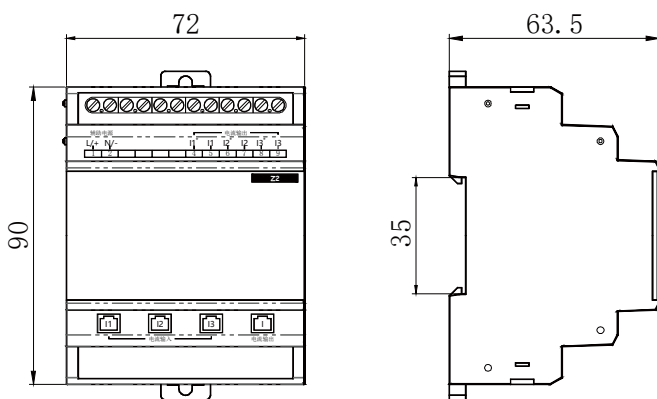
Внешний вид и габаритные размеры модуля коммутации Z2
